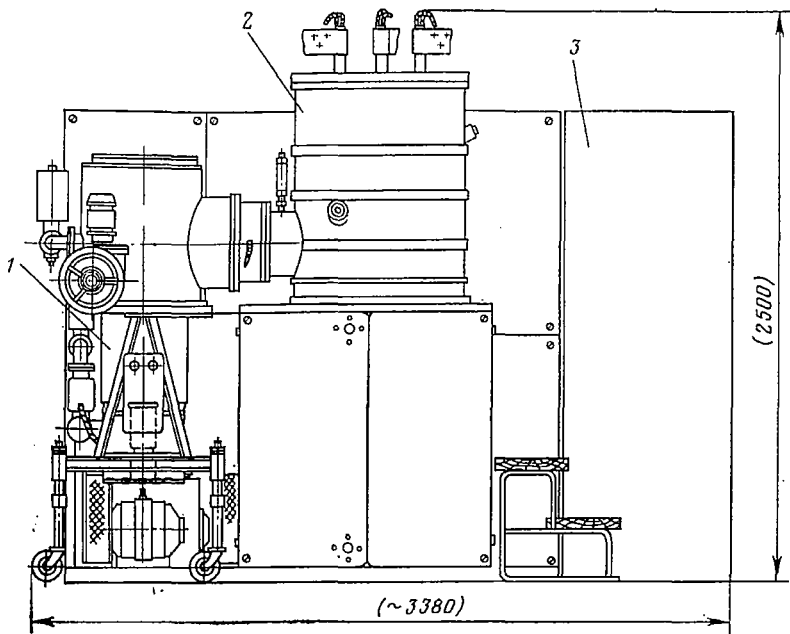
Общий вид электропечей ОКБ-8085 и ОКБ-8086 (габаритный чертеж).
